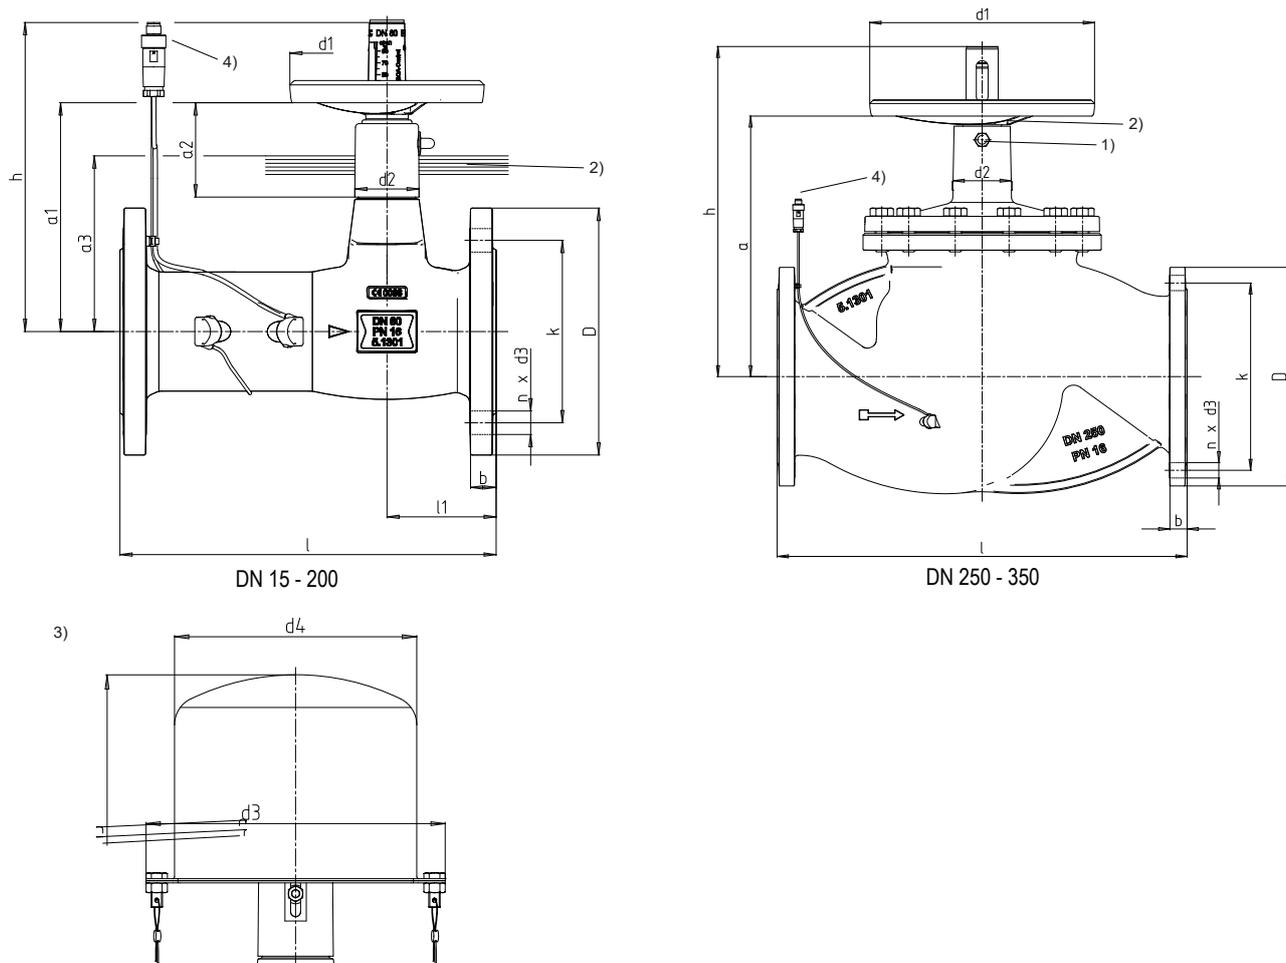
Dimensioni; BOA-CL DN 15 - 200, BOA-H DN 250 - 350
